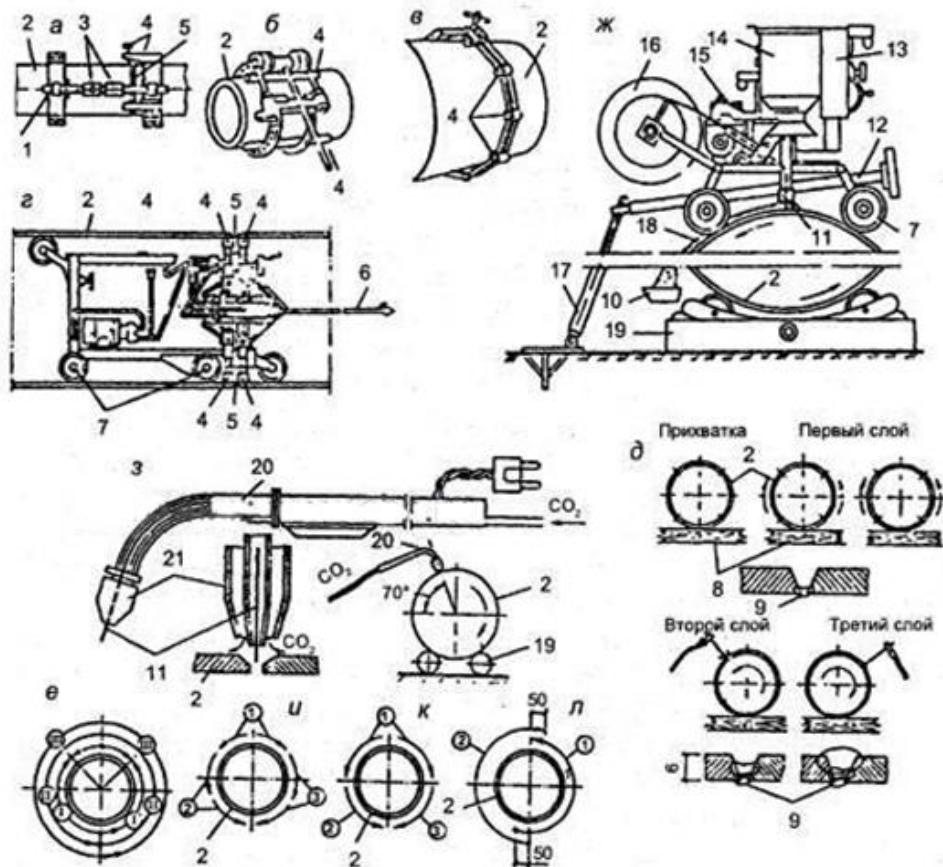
Сборка и сварка стальных труб:
